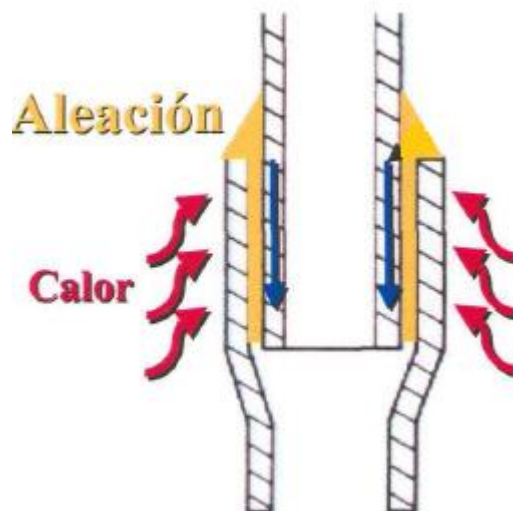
Acción de la Capilaridad en la Soldadura de Tubería [26].
